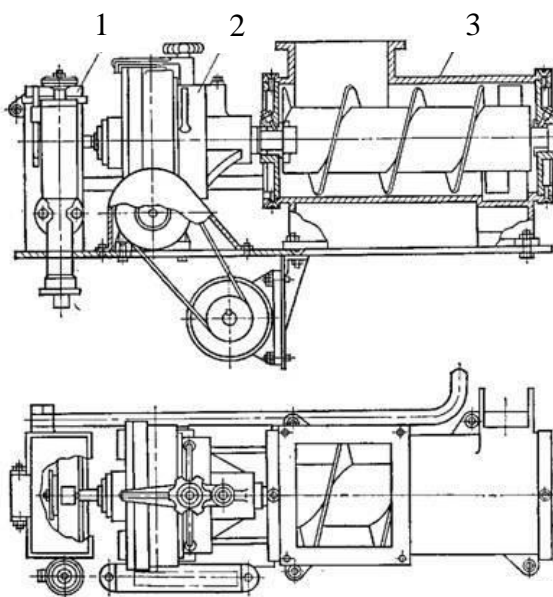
Конструктивні елементи макаронного преса: 1 – дозатор води; 2 – редуктор привода; 3 – шнековий дозатор
